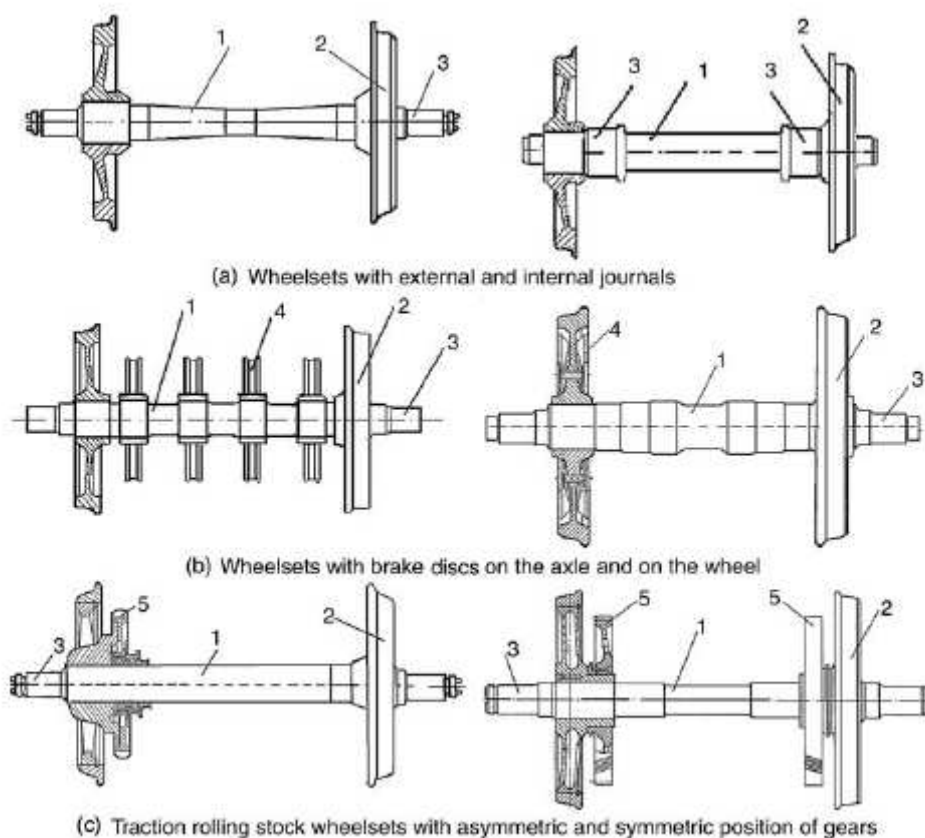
Principales tipos de diseños de eje montado: (a) con rodamientos externos e internos; (b) con discos de freno en el eje y en la rueda; (c) con posición asimétrica y simétrica de engranajes (1, eje; 2, rueda; 3, rodamiento; 4, disco de freno; 5, engranaje de dientes)
